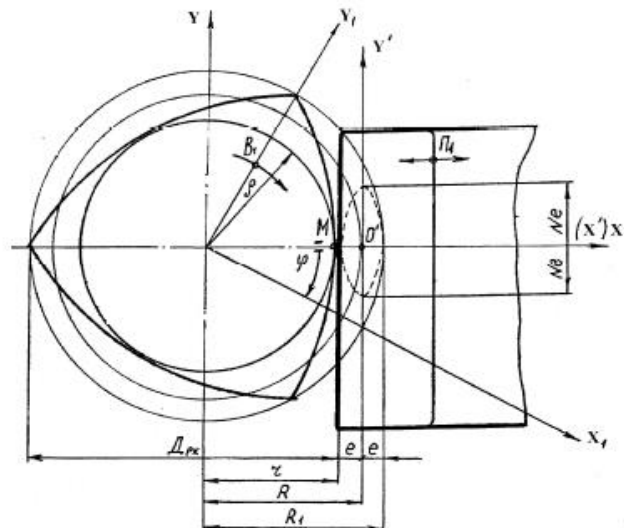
Однокоординатна схема обробки РК-профілю
